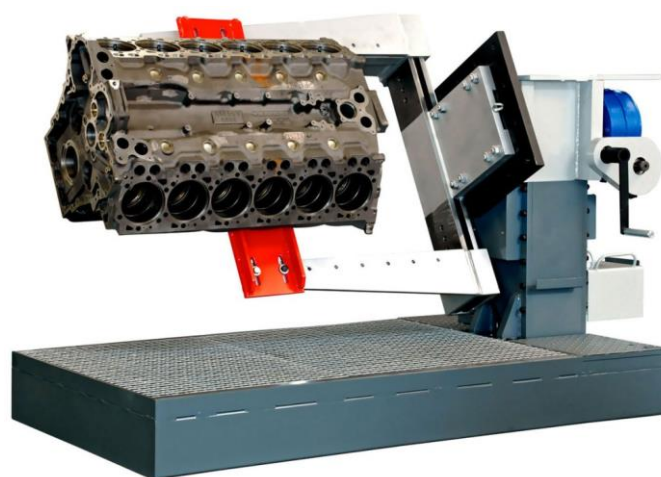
Стенд для переборки двигателей WW-HV-2500
